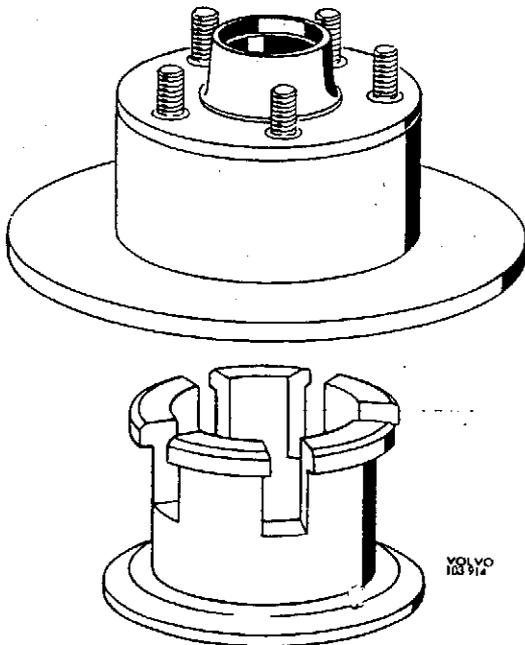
Einrichten der Bremsscheibe auf dem Werkzeug
